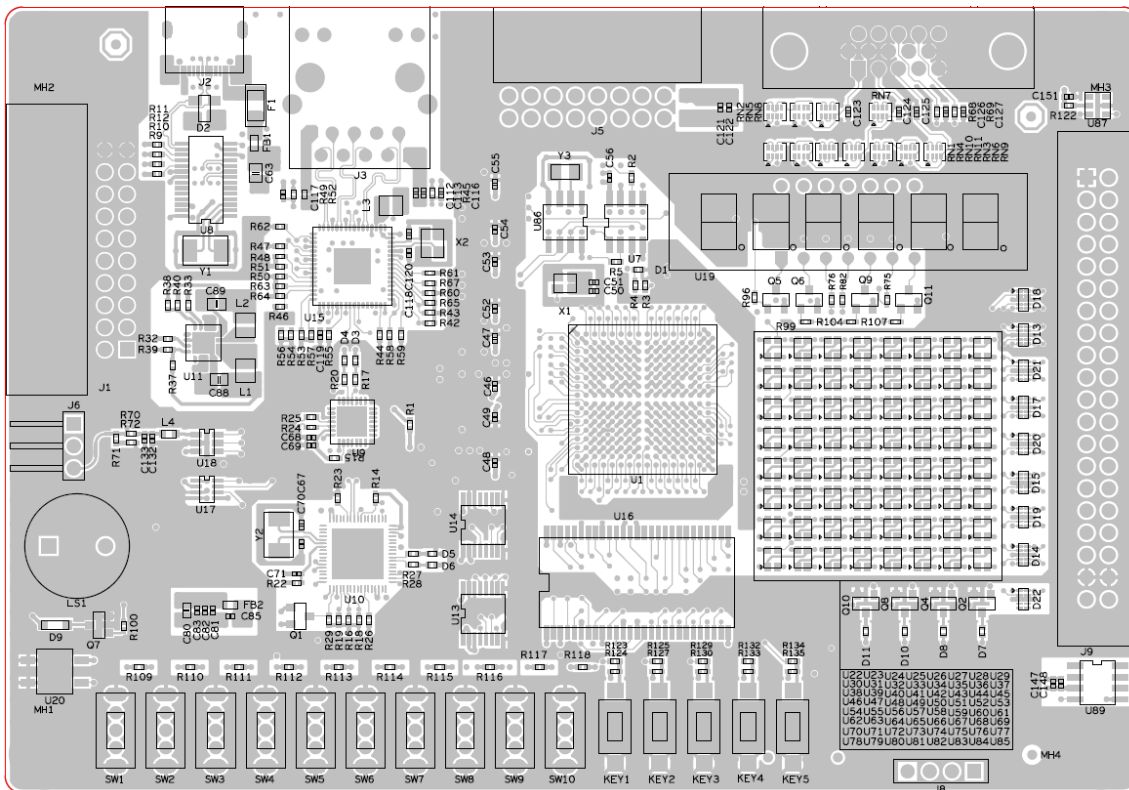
AWC_C4MB 开发板 PCB 图（背面、带位号）
